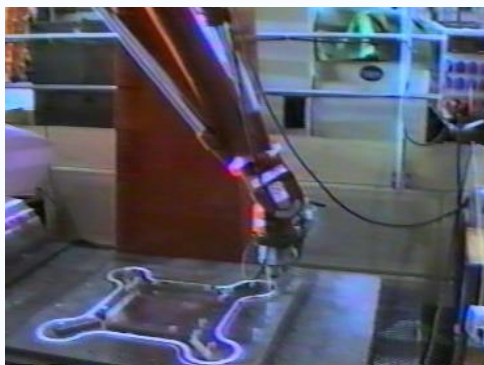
Robot realizando un proceso de Soldadura por Fricción y Agitación no lineal
